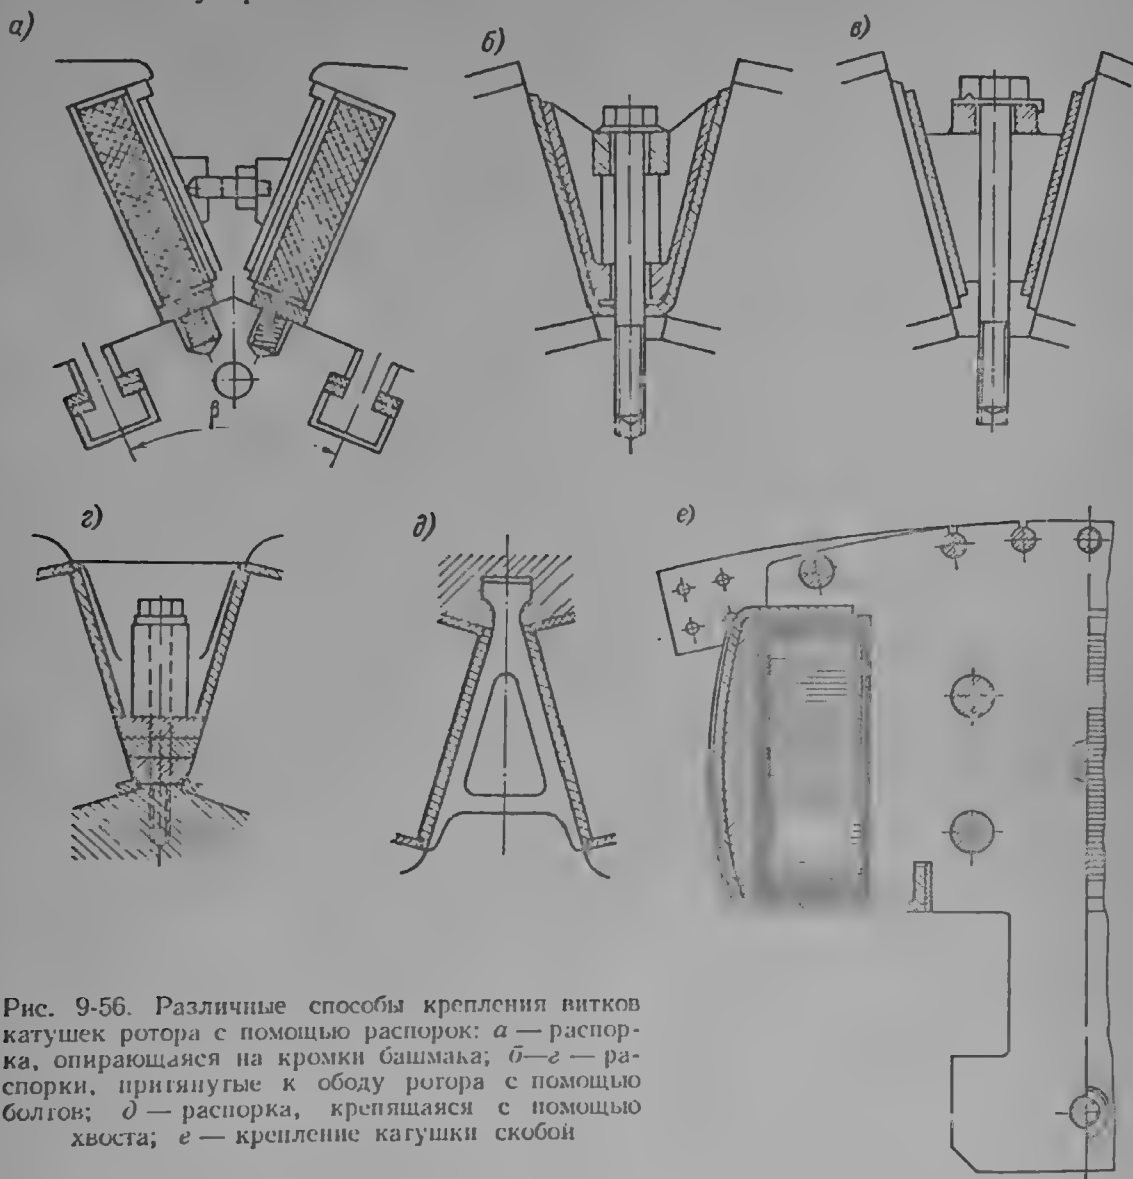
Различные способы крепления витков катушек ротора с помощью распорок: а — распорка, опирающаяся на кромки башмака; б—г — распорки, притянутые к ободу ротора с помощью болтов; д — распорка, крепящаяся с помощью хвоста; е — крепление катушки скобой
